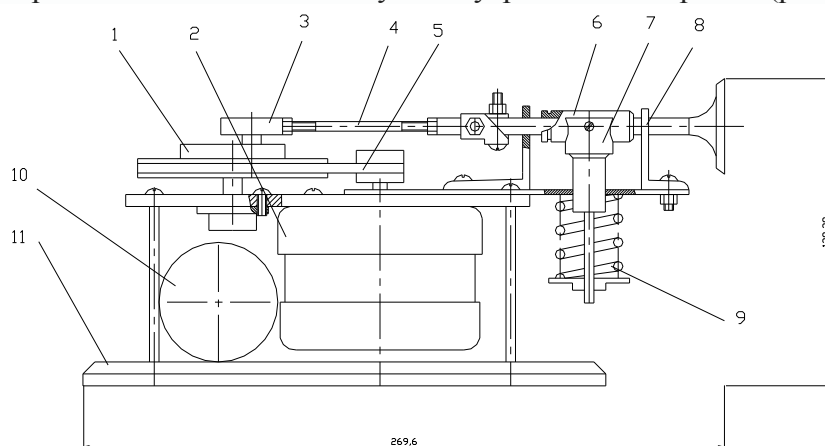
Установка для випробувань на зношування клапанів ДВЗ
